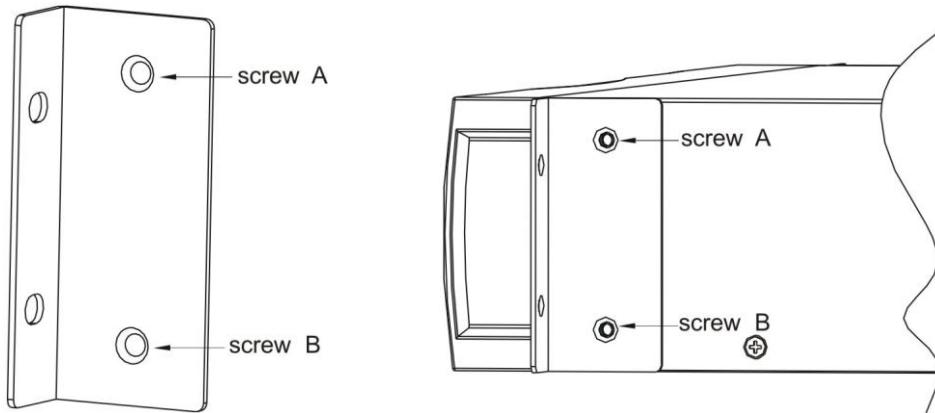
Деталь стойки консоли Рис. 12 Сборка стоики консоли
